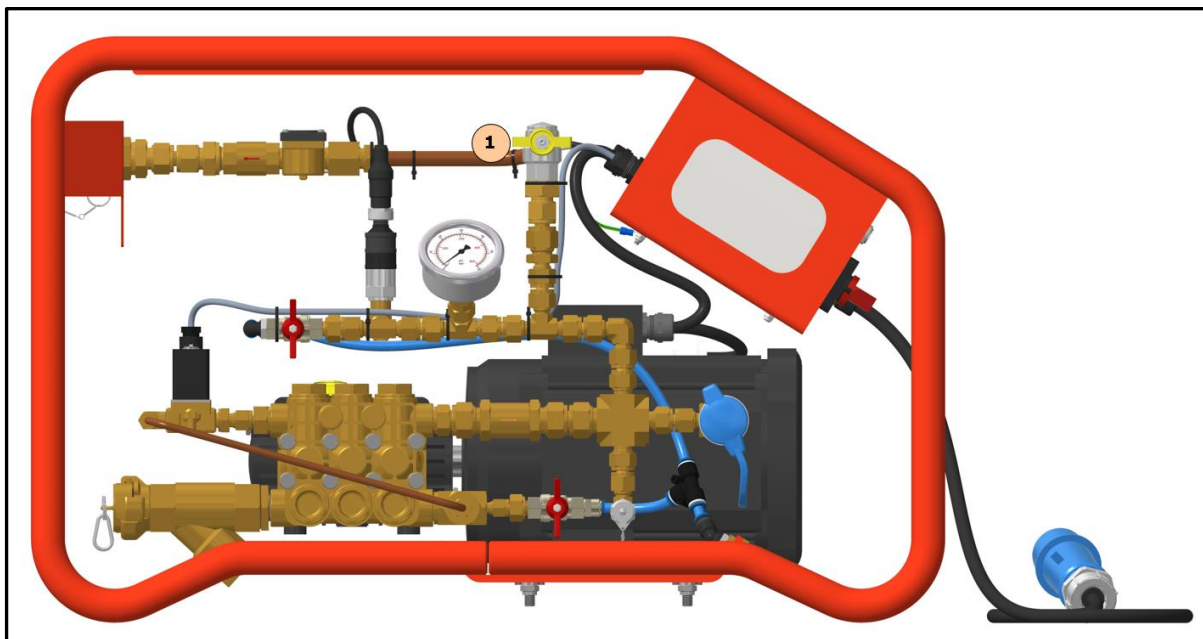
Bedienelemente Druckablassvorrichtung mit Wassermengenmessung
